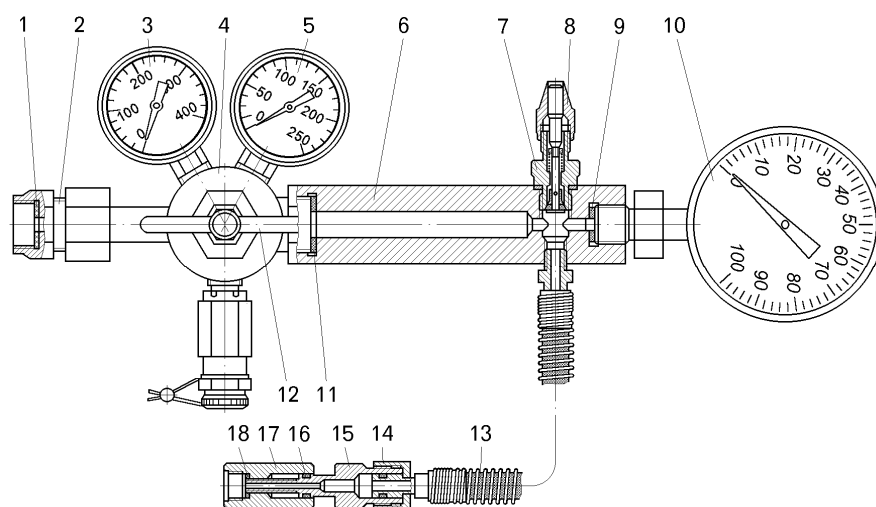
Приспособление для зарядки цилиндров подвески:
